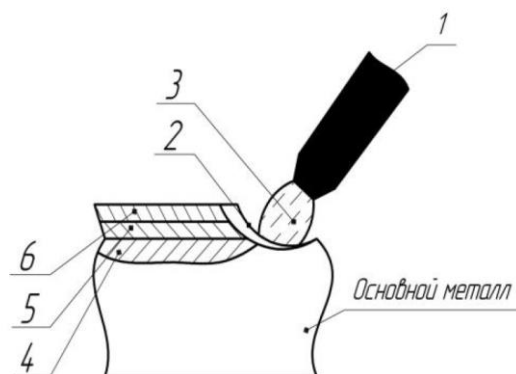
Схема выполнения ручной дуговой наплавки
